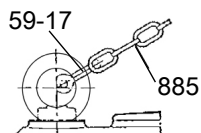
Befestigung der Kette mit Schäkel an der Ringschraube
